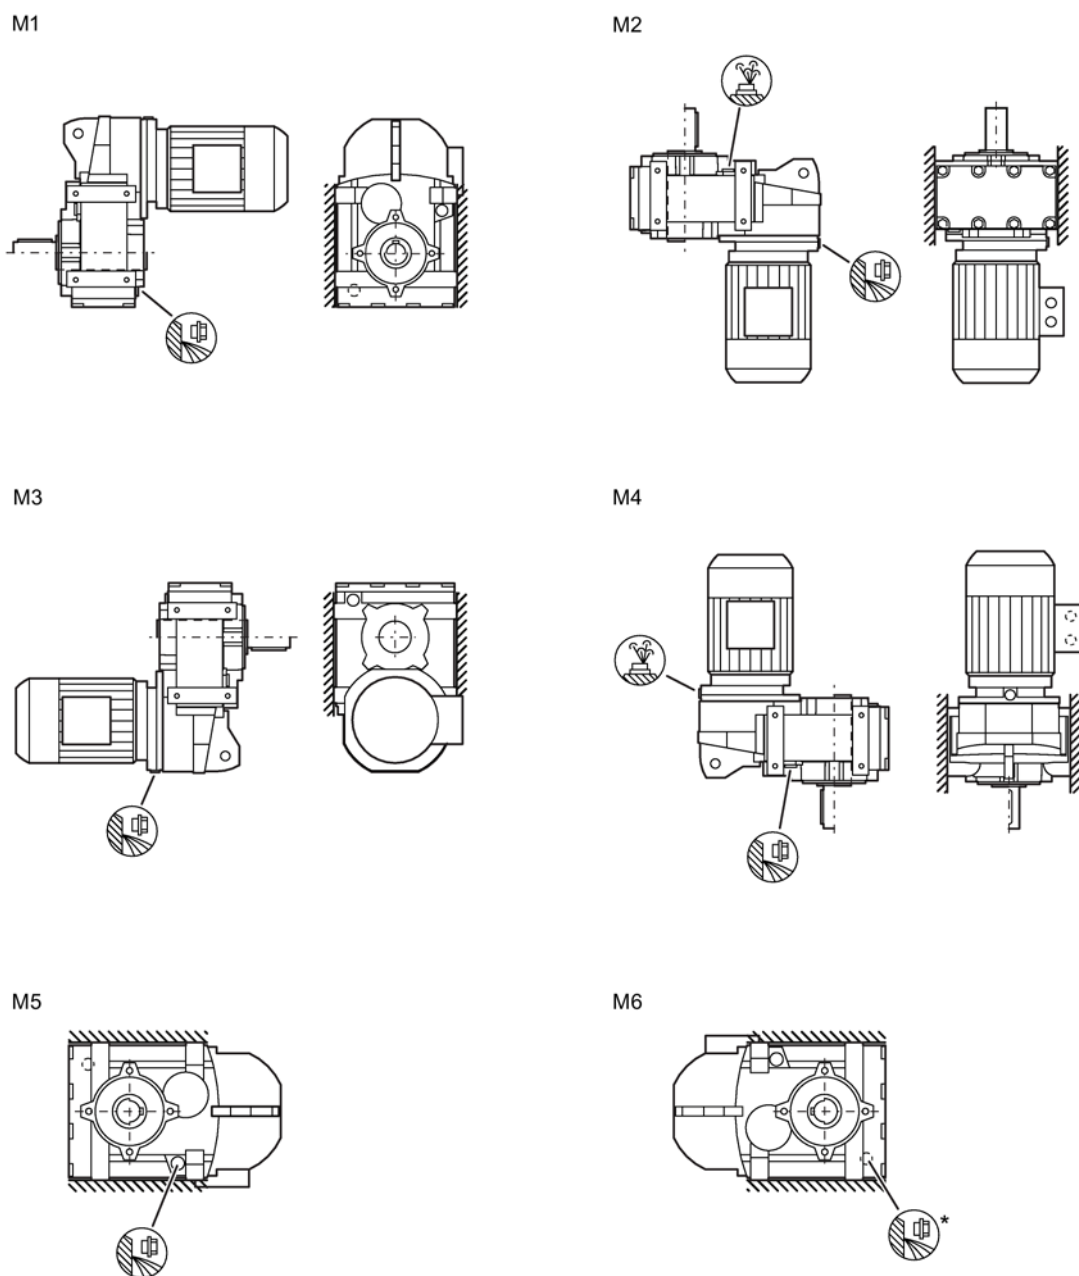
Монтажные положения для плоского редуктора F, в исполнении на лапах, типоразмер 29
